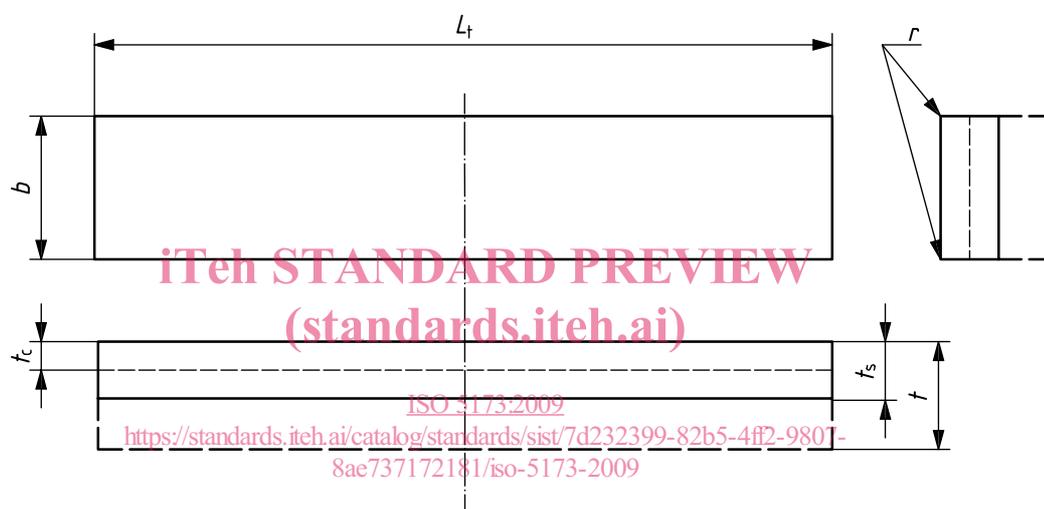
Éprouvette de pliage droit sur revêtement sans soudure bout à bout (FBC)
